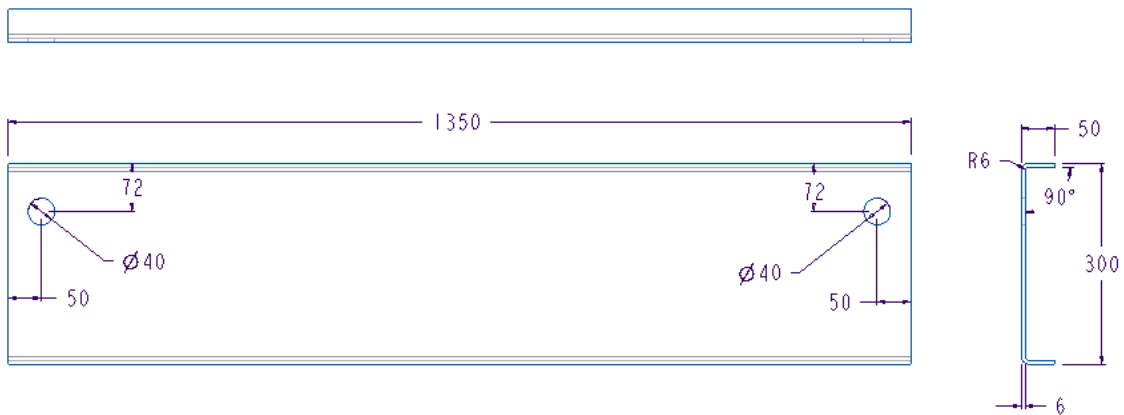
Dibujo dimensional de la parte B. Vistas ortogonales. Cotas en mm.
